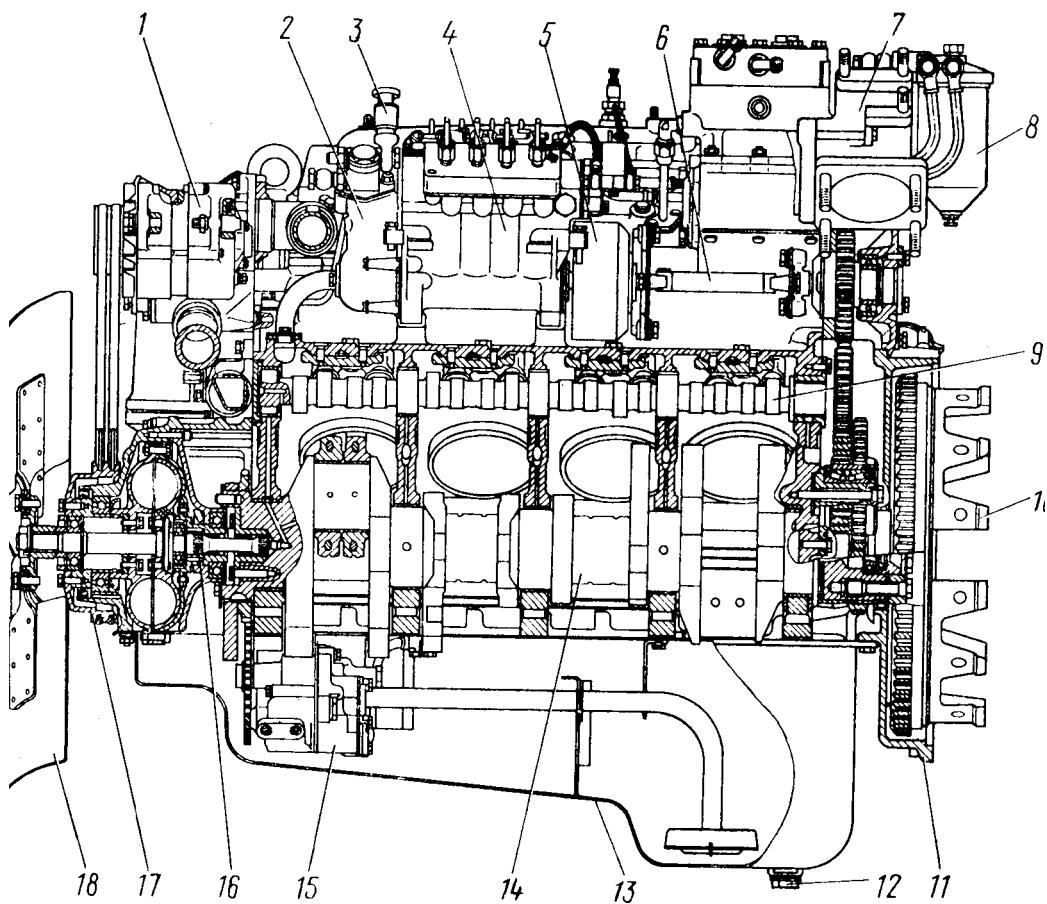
Продольный разрез двигателя КамАЗ-740.10: 1 - генератор; 2 - насос топливный низкого давления; 3 - насос топливоподкачивающий ручной; 4 - насос топливный высокого давления; 5 - муфта автоматическая опережения впрыскивания топлива; 6-полумуфта ведущая привода топливного насоса высокого давления; 7-патрубок соединительный выпускных воздухопроводов; 8 - фильтр тонкой очистки топлива; 9 - вал кулачковый; 10 - маховик; 11 - картер маховика; 12-пробка сливная; 13-картер двигателя; 14-вал коленчатый; 15 - насос масляный; 16 - валик привода ведущей части гидромуфты; 17 - шкив привода генератора; 18-крыльчатка вентилятора
